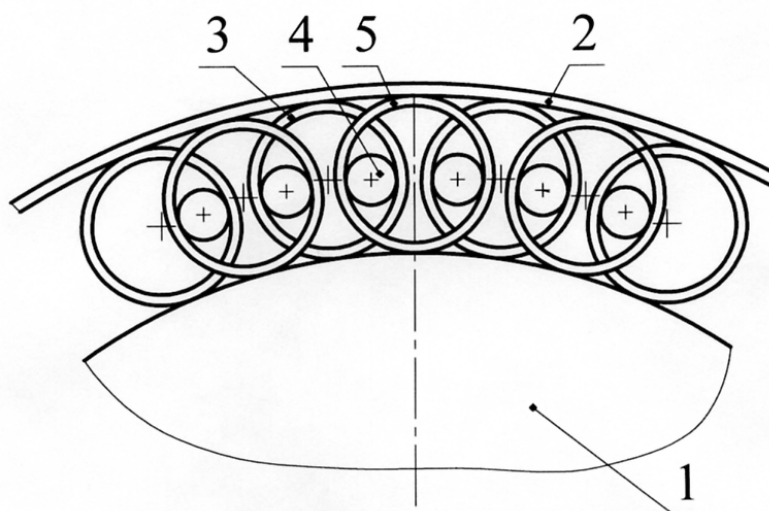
Бессепараторный подшипник (US 4053191, E. Traut)
